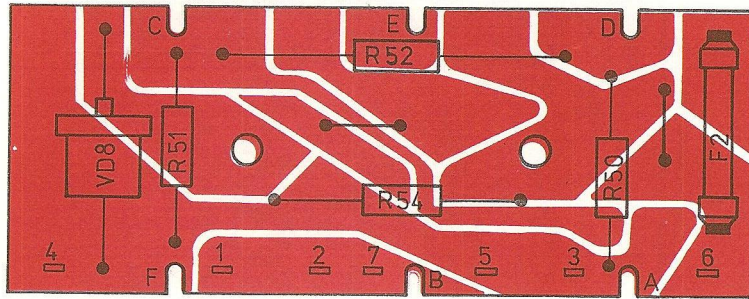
Deska elektronické pojistky 3AK 060 49 (strana spojů)
